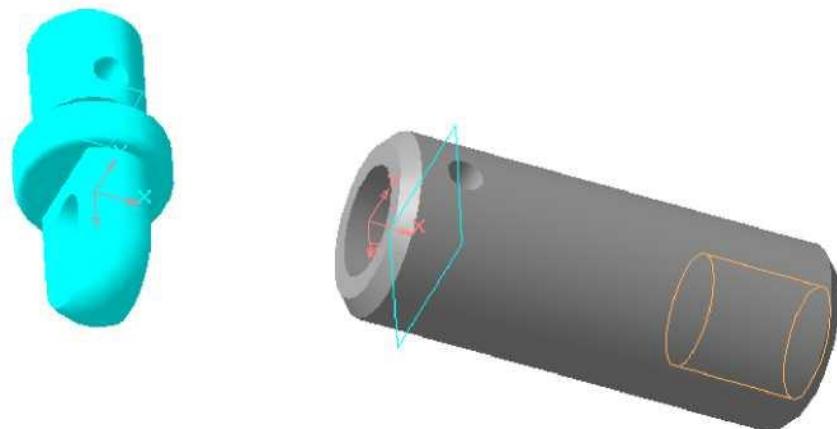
Подсборка из деталей *Корпус* и *Палец
